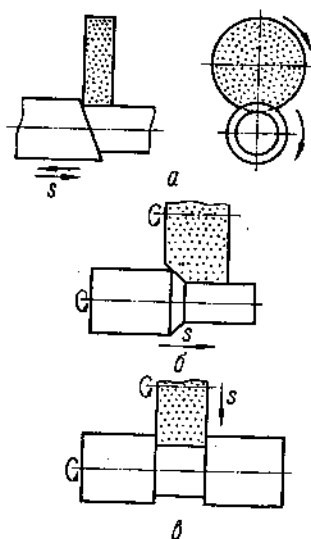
Схемы шлифования цилиндрических поверхностей:
